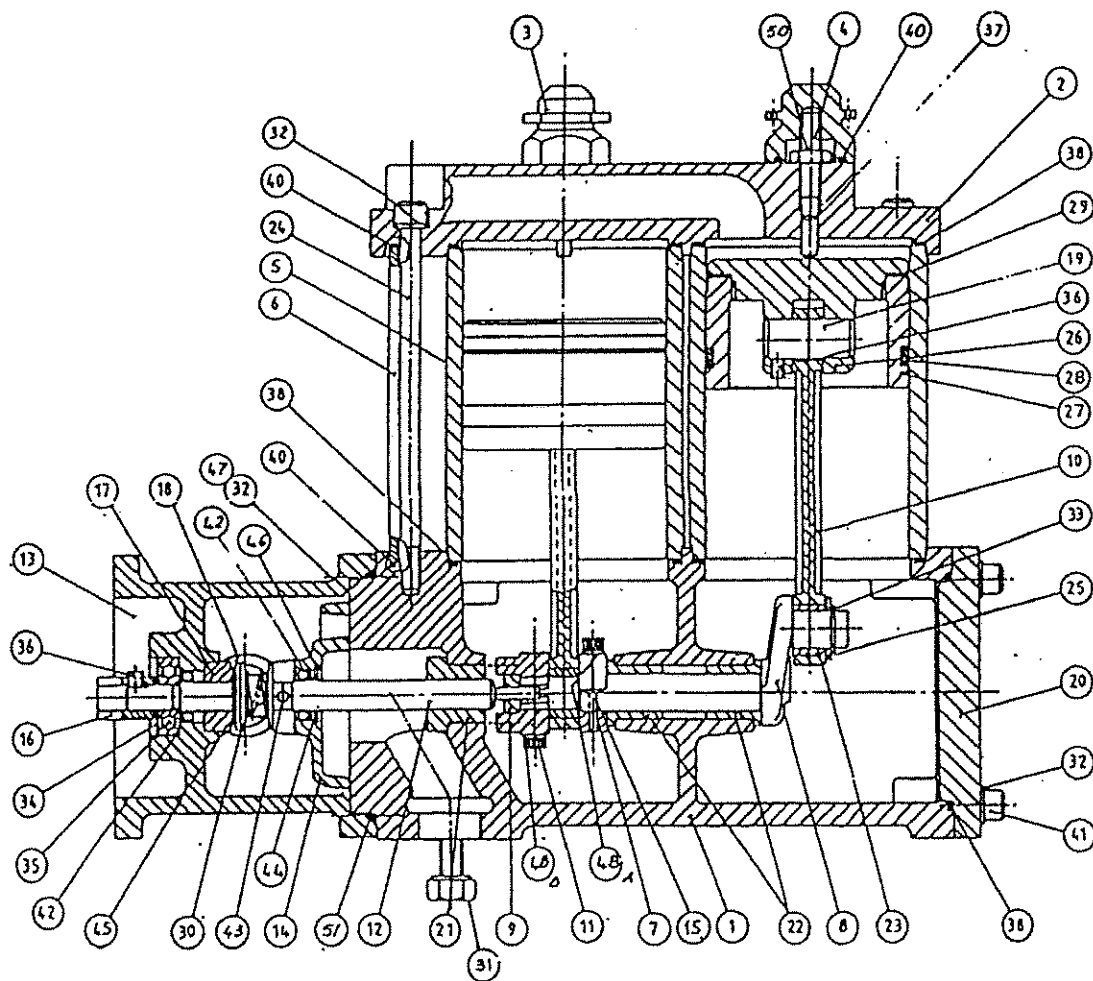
Hydraulická schéma stojana typu FAS 120
